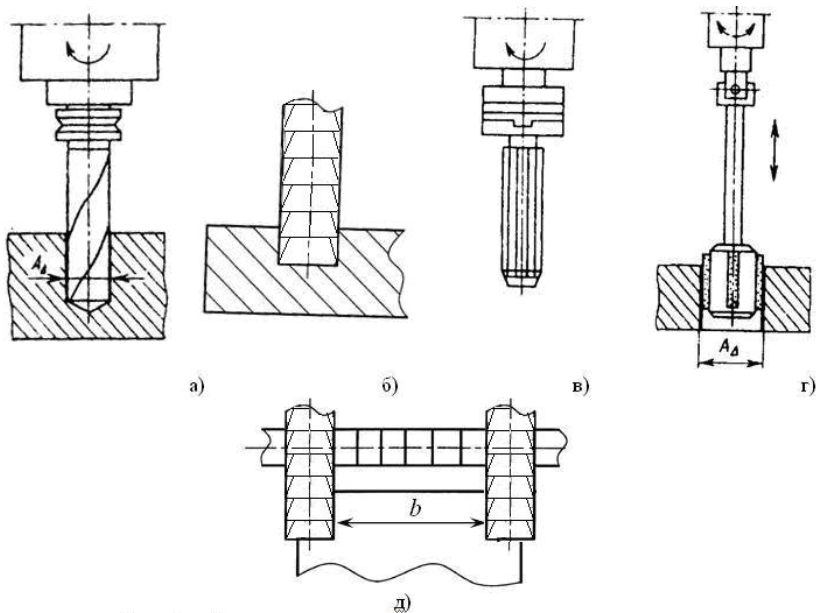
Схема получения размеров заготовки мерным инструментом:
